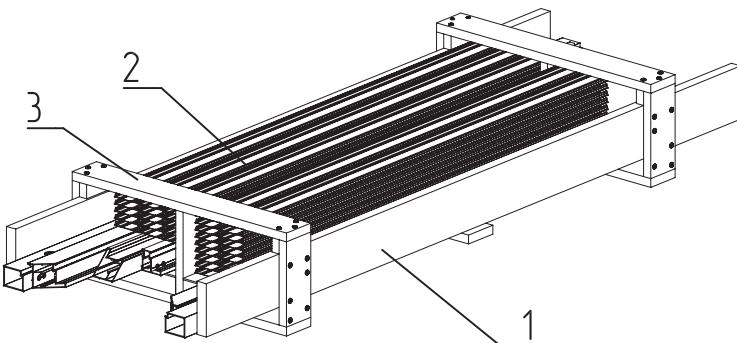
Упаковка деталей рамы калитки(FLGU.400.9803-01)
